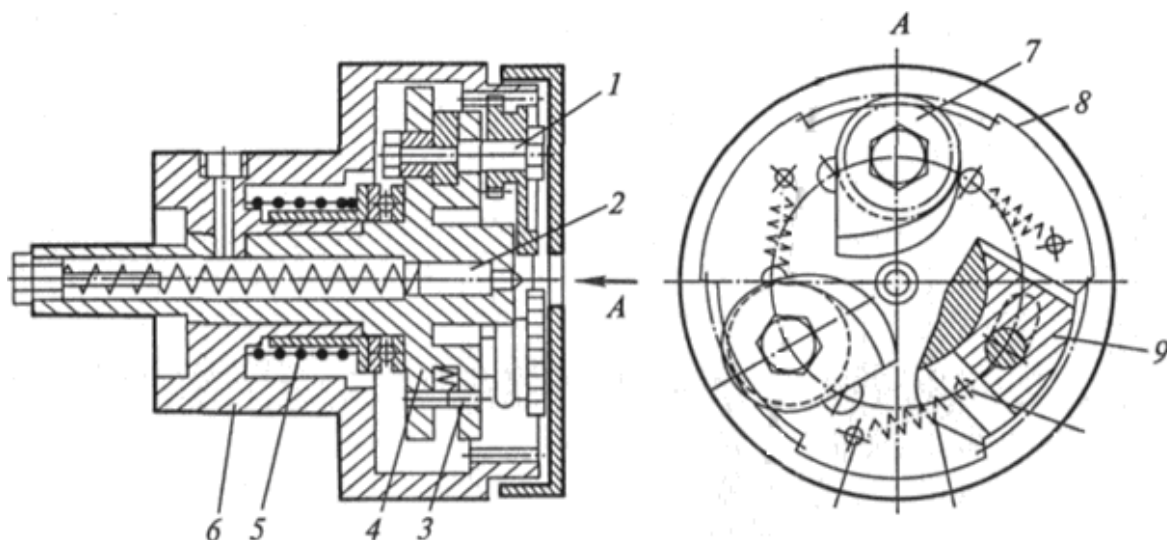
Повідковий самозатискний патрон: 1 – вісь; 2 – плаваючий центр; 3 – круговий паз; 4 – рухомий корпус; 5 – поворотна пружина; 6 – корпус; 7 – зубчасте колесо-кулачок; 8 – зубчастий сектор; 9 – вставка; 10, 12 – штифти; 11 – пружина
